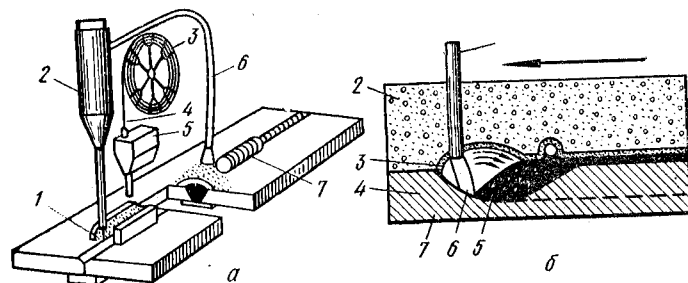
Схема автоматической сварки под слоем флюса (а) и продольного разреза зоны сварки (б)
